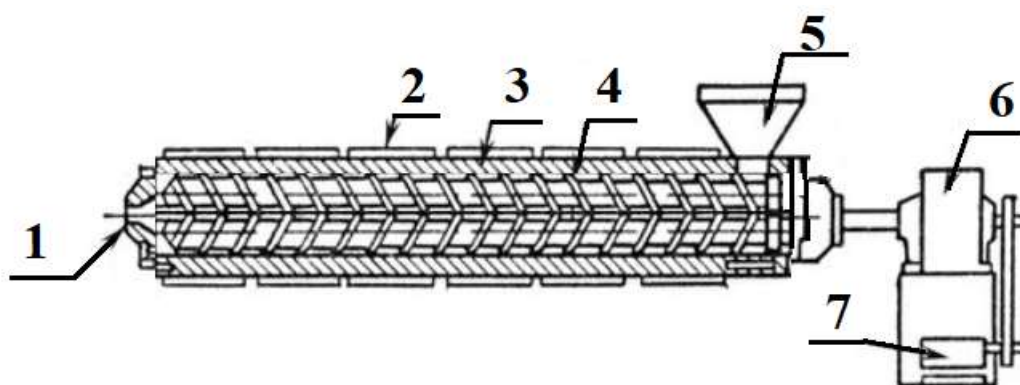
Схема двухшнекового горизонтального экструдера: 1 —экструзионная головка; 2 — нагреватели; 3 — корпус; 4 — шнеки; 5 —загрузочное устройство; 6 — редуктор; 7 — двигатель.
